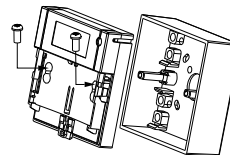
Крепежные элементы корпуса Извещателя и задней крышки
